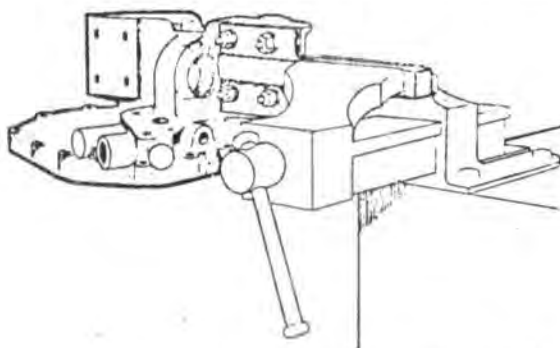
FINITION DU CARTER ARRIÈRE DANS L'ÉTAU (0° VUE)
